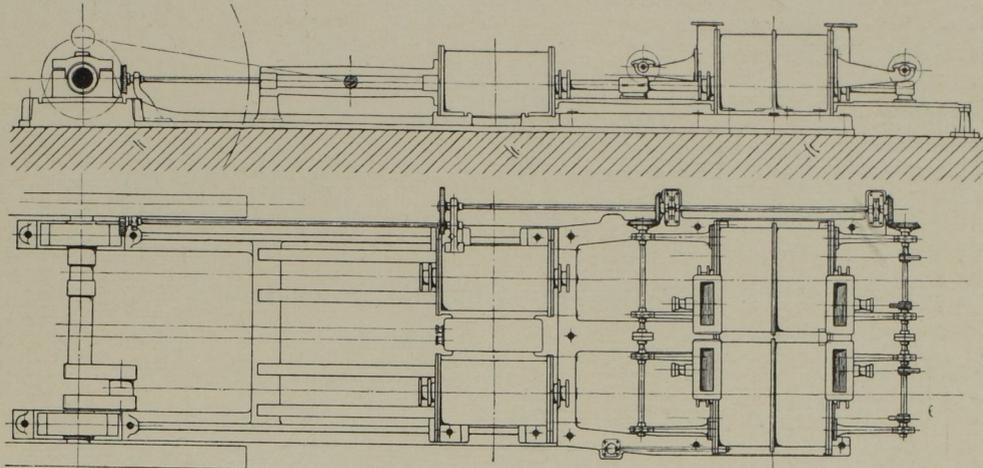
Seitenansicht und Grundriss. Massst. 1:100.
